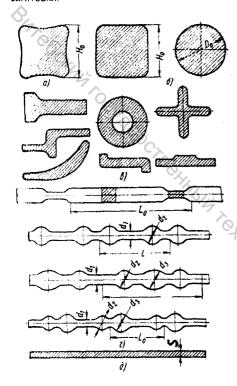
Типы прокатных профилей, применяемых для ковки и штамповки:
